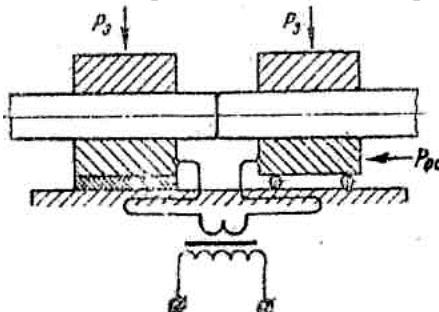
Схема процесса стыковой сварки:
